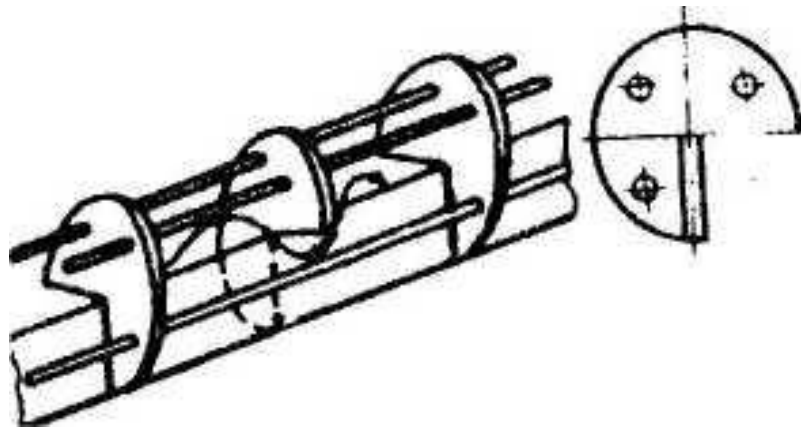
Конструктивная схема поперечных перегородок
